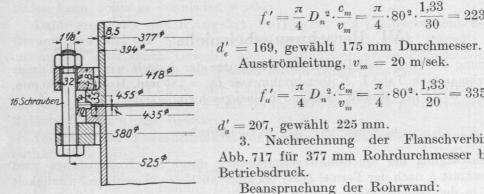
Lose Flanschverbindung für 377 mm Rohrdurchmeser.
